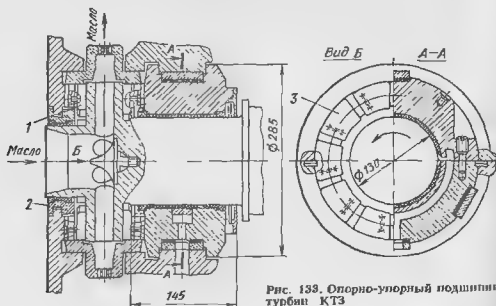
Опорно-упорный подшипник турбин КТЗ
